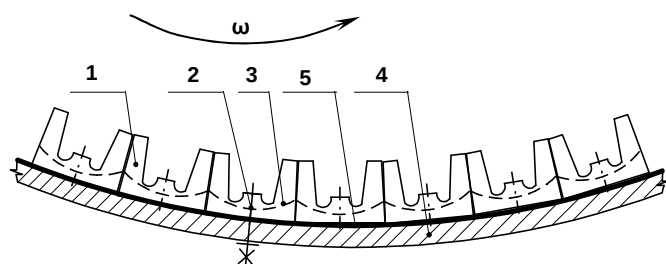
Способ укладки в профиль износа футеровки профиля «Коробчатая»: 1-футеровка профиля «Коробчатая»; 2-болт крепления футеровки; 3-профиль износа футеровки; 4-стенка барабана; 5-прокладка $\delta=6\div 8$ мм
